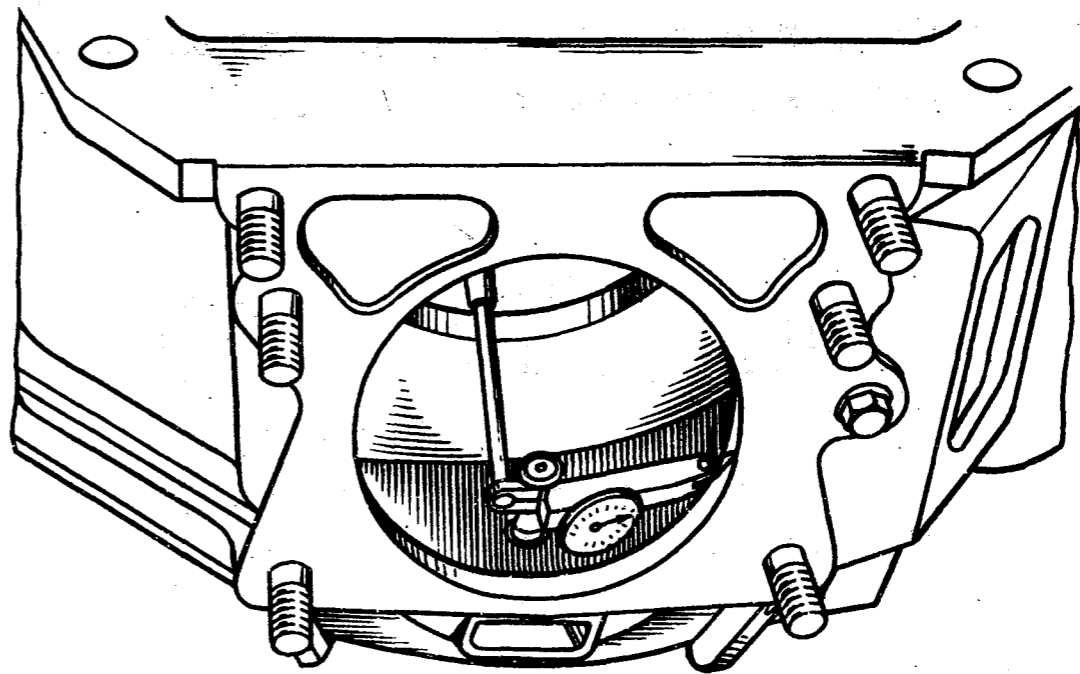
Проверка concentricity отверстия картера сцепления с осью коленчатого вала приспособлением 24-V-II4625
